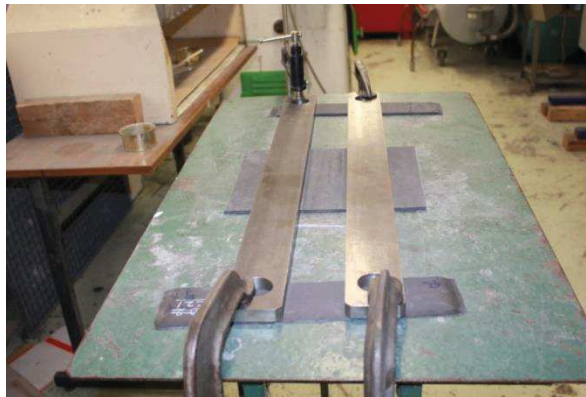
Mise en place des guides et de la plaque pour l'usinage
